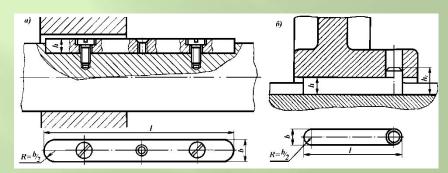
Подвижные соединения призматической шпонкой: *а)* направляющая шпонка;
